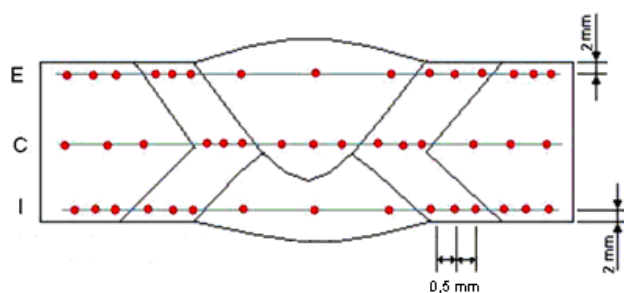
Local de medição da dureza Vickers das juntas soldadas. E = Superfície externa do tubo; C = Centro da espessura; I = Superfície interna do tubo
